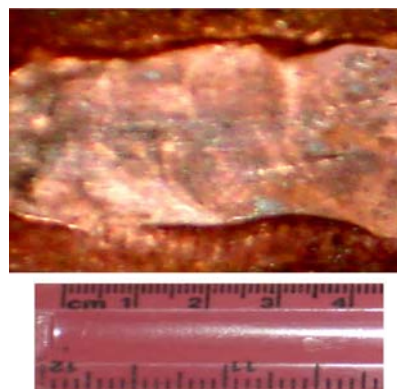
Прокатанный сварной шов меди со сталью
